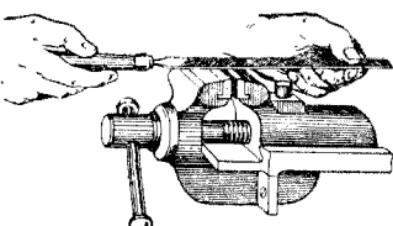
Тримання напилка при обпилуванні великих деталей.
